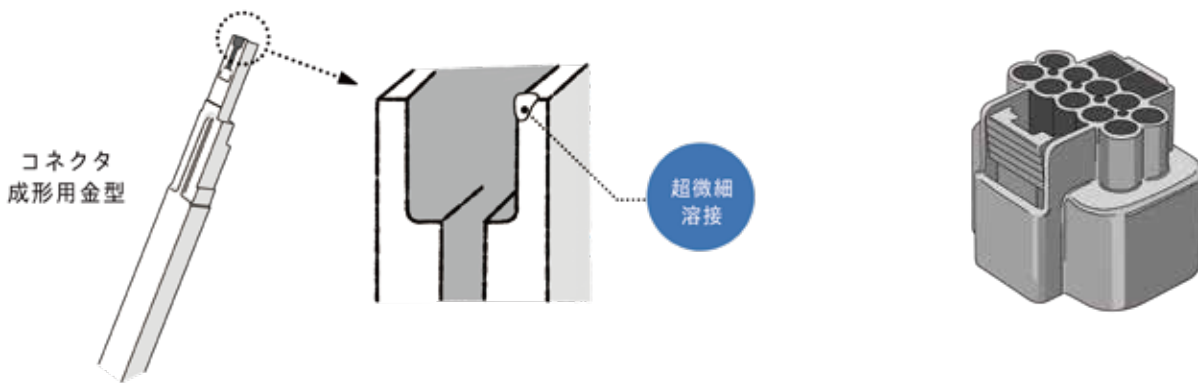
コネクタ成形用金型への超微細溶接
